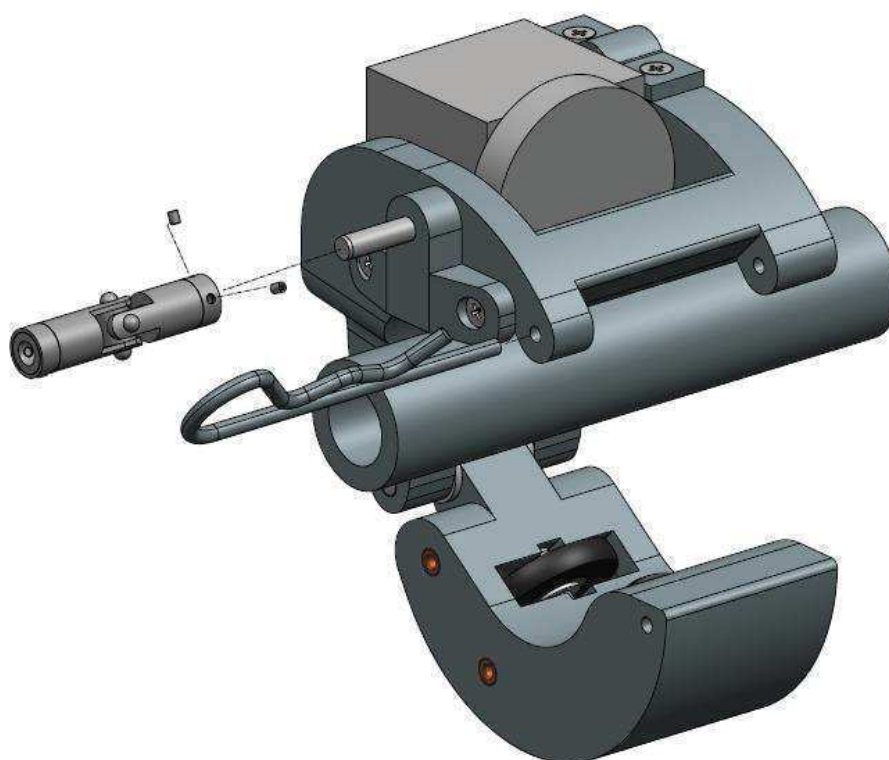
Montáž připojení pro část s enkodérem na přední část manipulátoru
